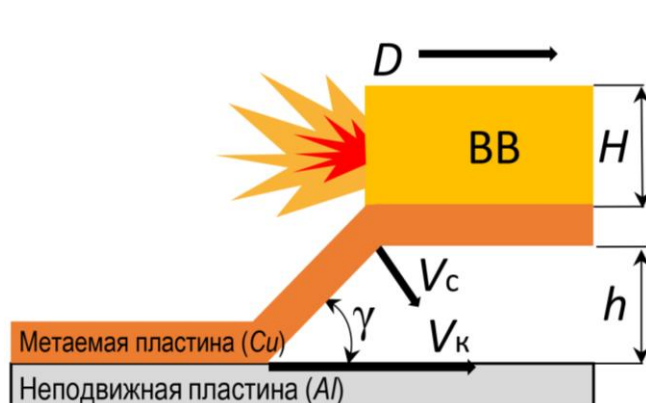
Схема соударения пластин при сварке взрывом:
